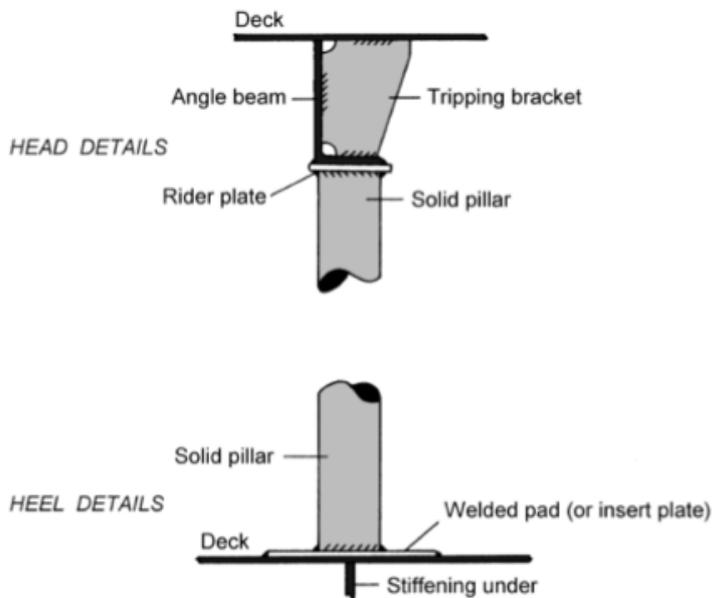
Configuración estructural y detalles – escuadra de conexión inferior
